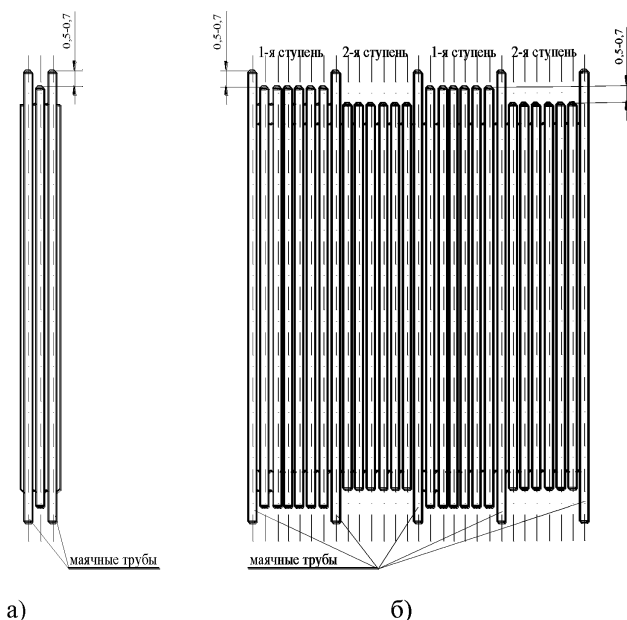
Подготовка панелей под сварку (разбивка по ступеням обработки)
